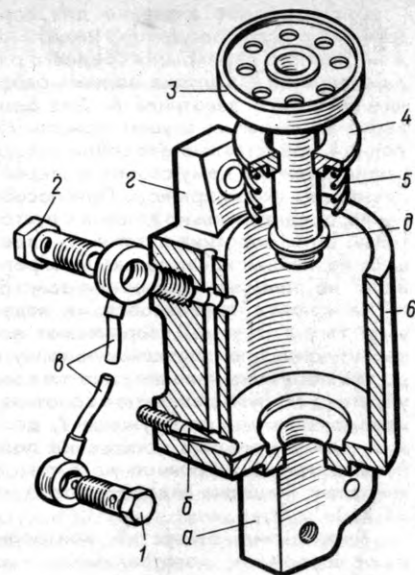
Компенсатор неравномерности хода: 1, 2 — штуцеры; 3 — поршень со штоком; 4 — тарелка; 5 — пружина; 6 — корпус компенсатора
